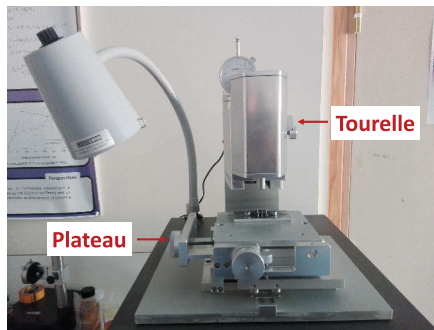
Machine de préparation de surfaces (ASAP) utilisée pour l'usinage mécanique en face arrière.
